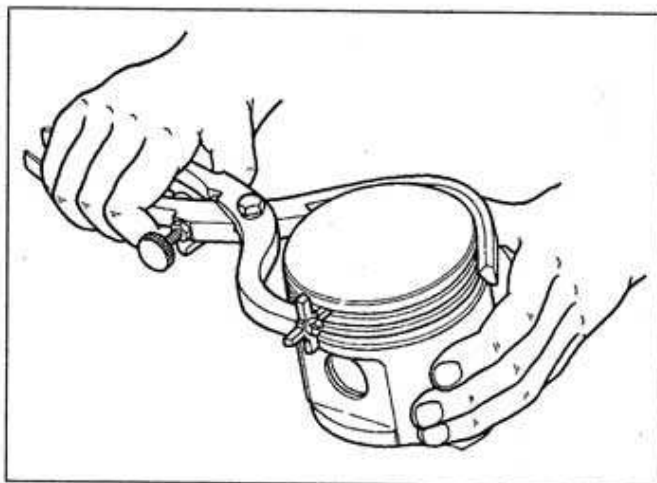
Очистка нагара в канавках поршней с помощью приспособления 5–У–27691
